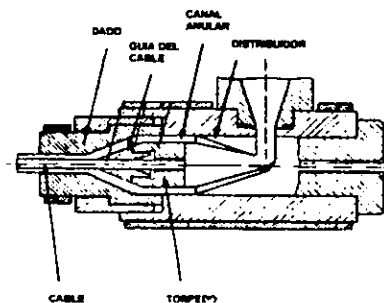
Nomenclatura del Cabezal de Recubrimiento de Cable.
